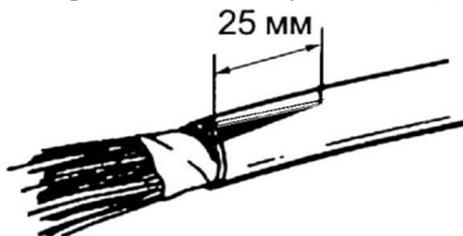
Разрезание оболочки для установки соединителя 4462.
